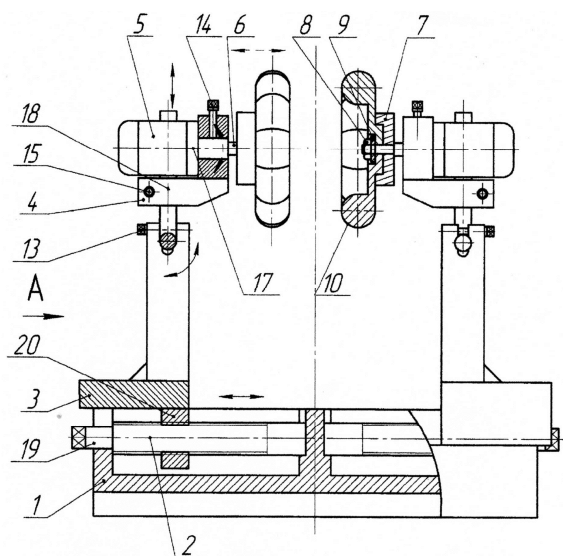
Устройство для магнитно-абразивной обработки патент RU №2220836
